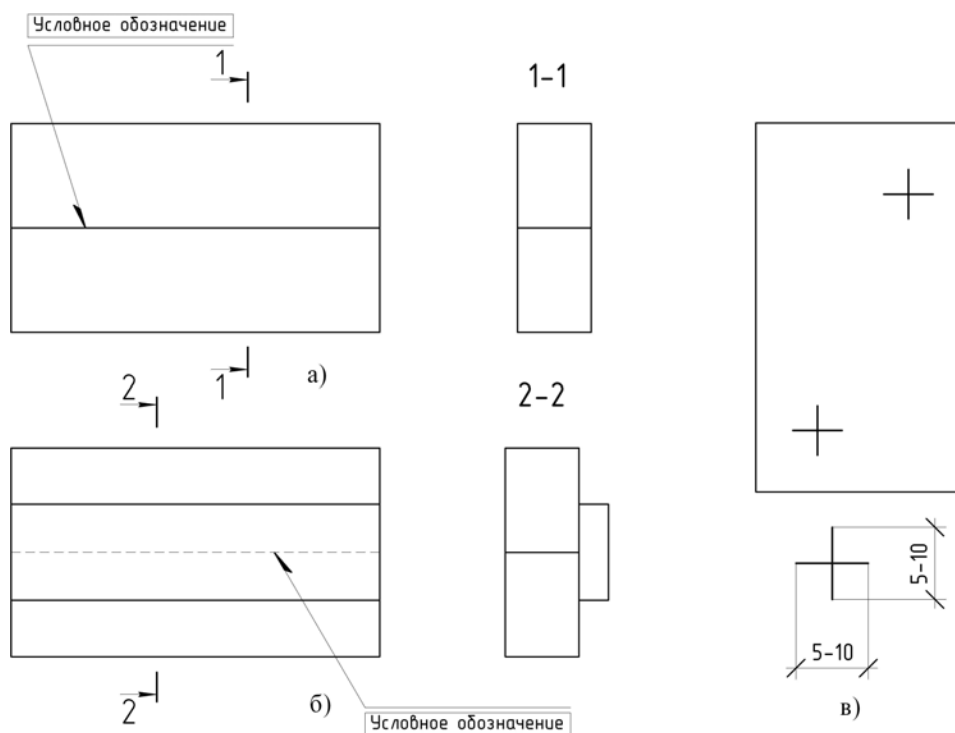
(а, б, в). Обозначение сварных швов
